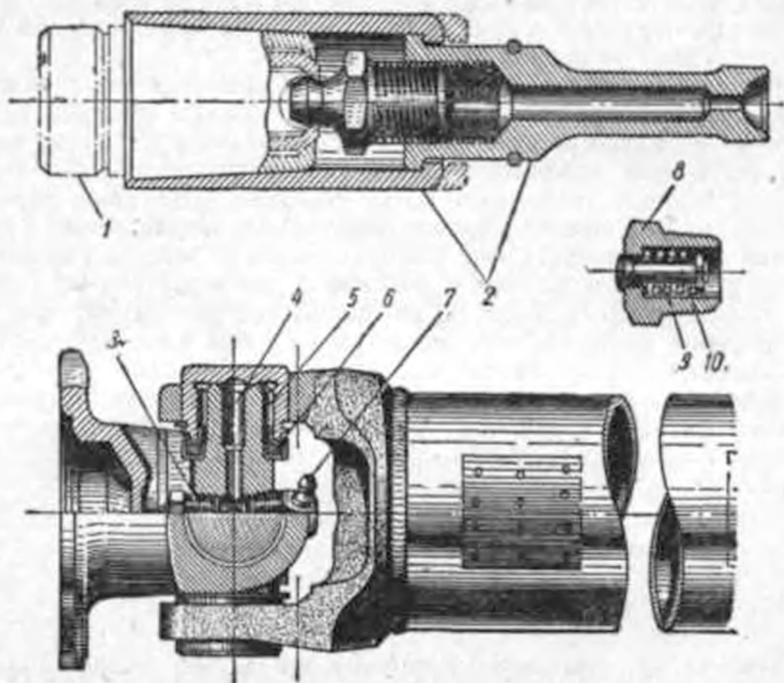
Расположение пресс-масленки и предохранительного клапана на крестовине карданного шарнира:
